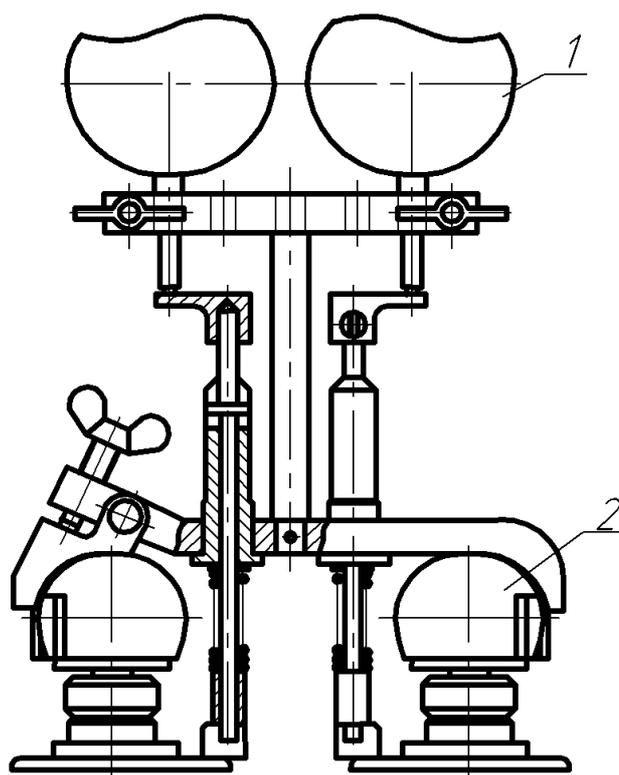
Приспособление для измерения зазора «на масло» в гидротолкателях: 1 – индикатор часового типа; 2 – опора на гидротолкателях
